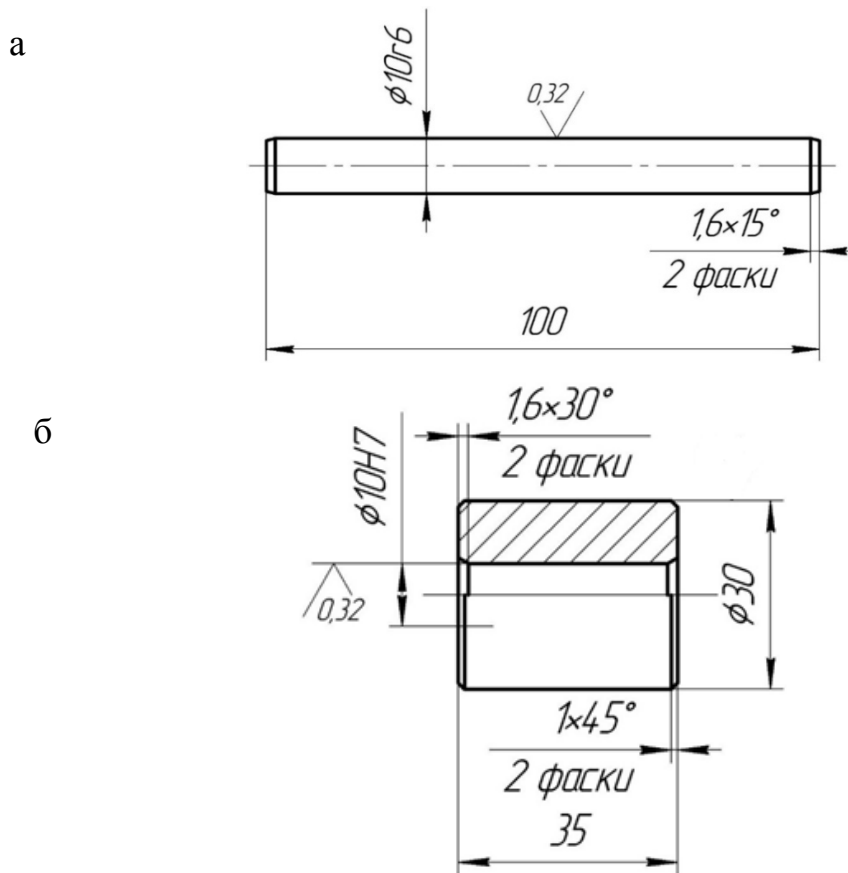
Конструкция образцов деталей соединения с натягом
